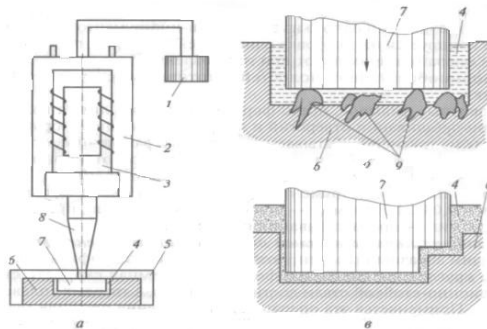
Схема ультразвуковой размерной обработки при прошивании (долблении): *а* — принципиальная схема ультразвуковой установки; *б* — схема съема материала при ультразвуковом прошивании; *в* — схема копирования профиля инструмента в заготовке; *1* —
